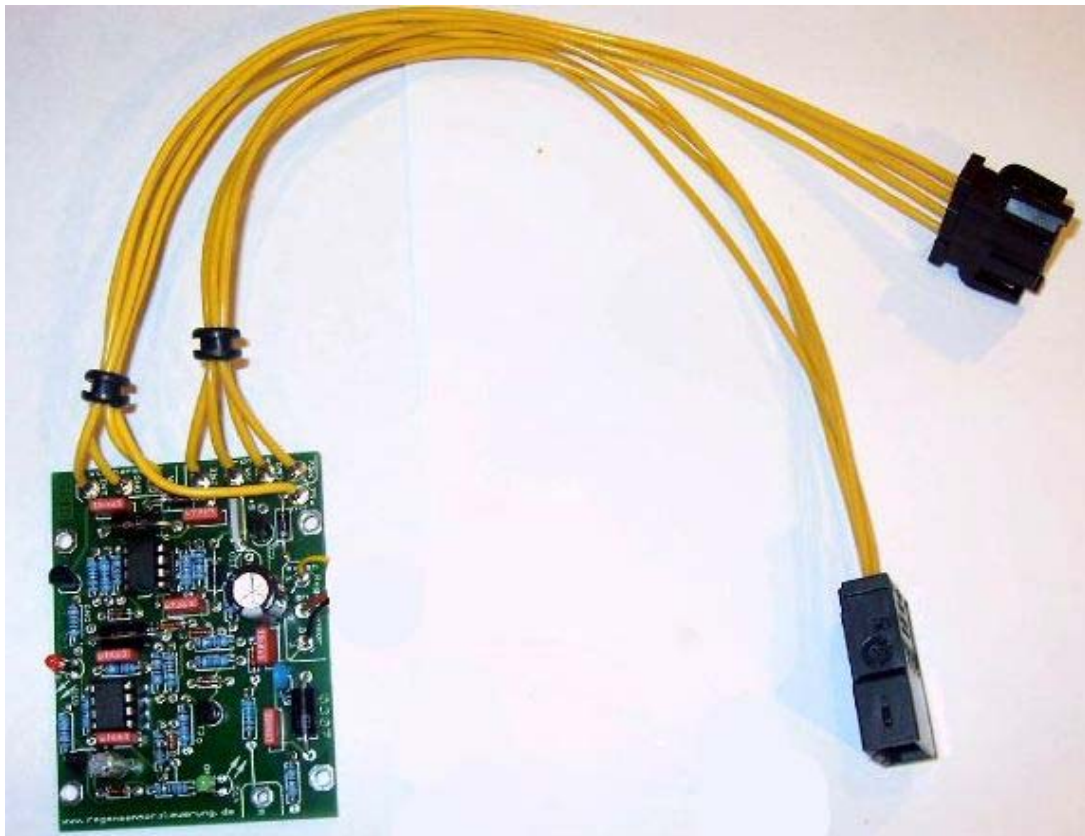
Platine mit angelöteten Anschlussleitungen für Bordnetz und Motor (exemplarisch ohne Anschlüsse für Regensensor oder Rückfahrtsignal)
